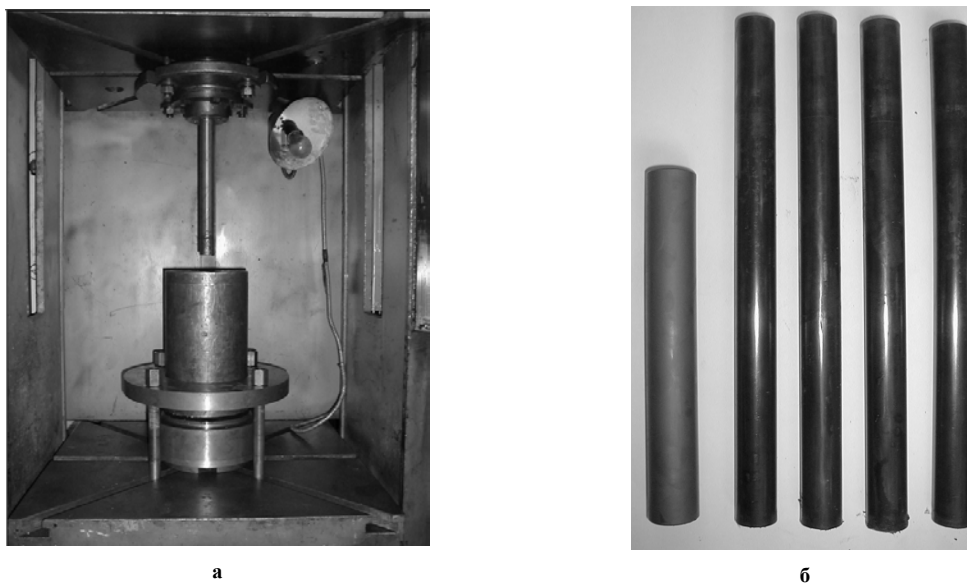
Виробничий штамп для видавлювання (а), вихідна заготовка та здеформовані заготовки (б)
